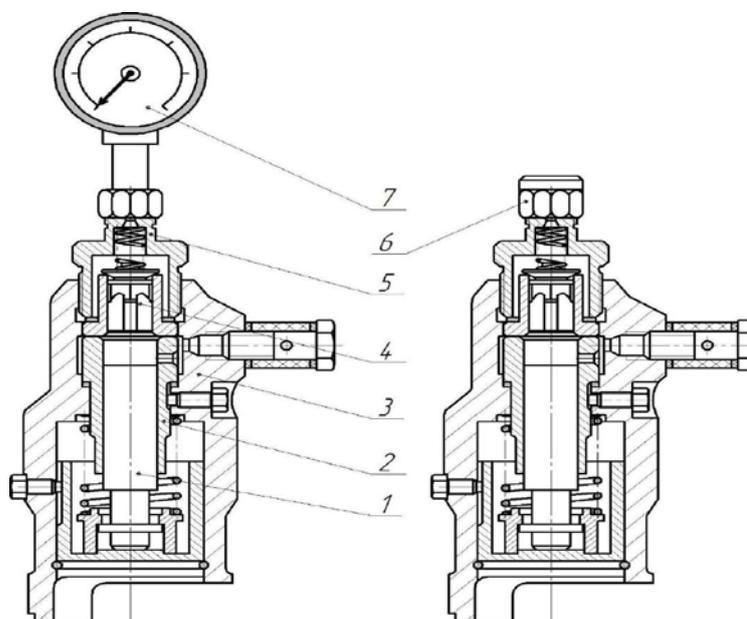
Проверка герметичности плунжерной пары и нагнетательного клапана ТНВД 1 - Плунжер; 2 - Направляющая втулка плунжера; 3 - Корпус ТНВД; 4 - Нагнетательный клапан; 5 - Нагнетательный штуцер; 6 - Заглушка; 7 - Манометр
